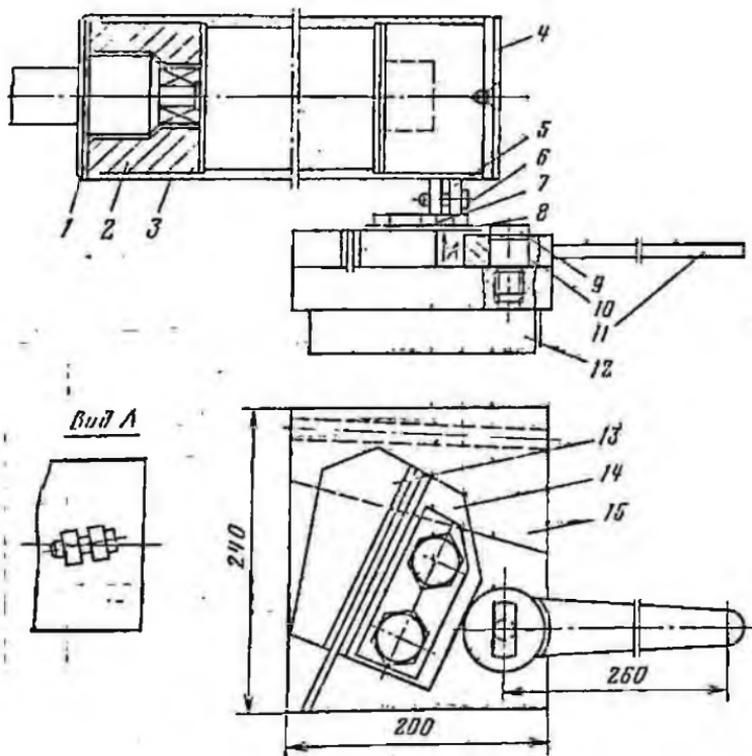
Приспособление для навивки шнековой спирали из полосовой стали на токарном станке:
